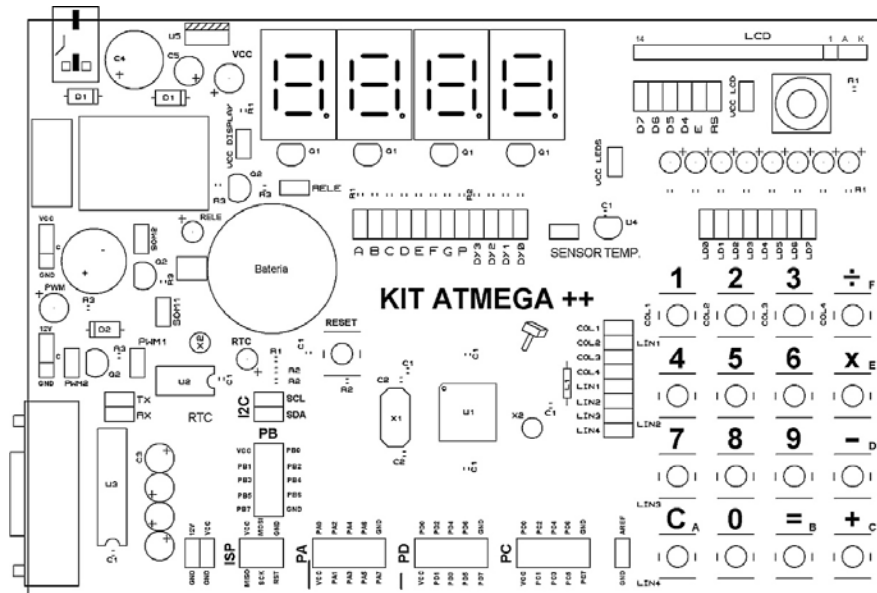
Desenho da parte a ser impressa sobre a parte superior da PCI (kit ATmega++).
